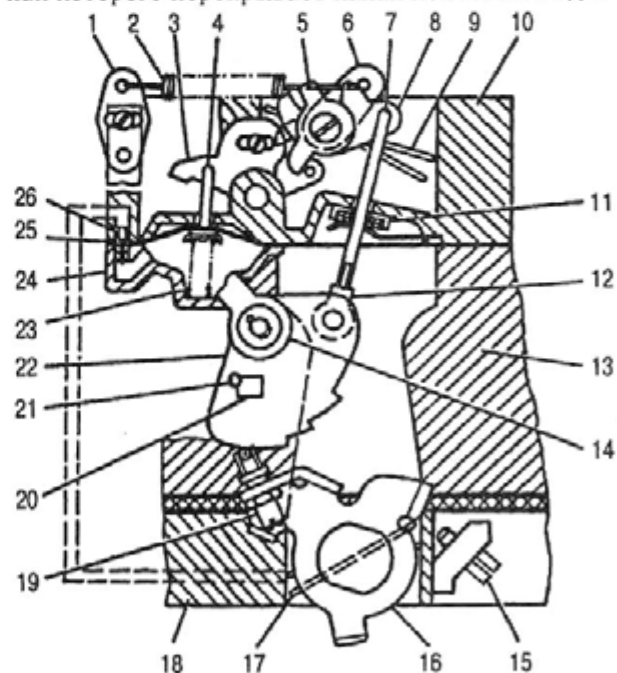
Система пуска и прогрева холодного двигателя: 1, 5, 6 и 16 - рычаги; 2 - пусковая пружина; 3 - промежуточный рычаг; 4 - тяга пневмокорректора; 7 - тяга; 8 - секторный рычаг; 9 - воздушная заслонка; 10 - крышка карбюратора; 11 - уплотнительный элемент; 12 - регулировочная муфта; 13 - корпус поплавковой камеры; 14 - рычаг привода воздушной заслонки; 15 - упорный винт дроссельной заслонки первичной секции карбюратора; 17 - дроссельная заслонка первичной секции карбюратора; 18 - корпус смесительных камер; 19 - винт с роликом; 20 - упор; 21 - штифт; 22 - профильный рычаг; 23 - пружина пневмокорректора; 24 - крышка пневмокорректора; 25 - диафрагма; 26 - жиклер пневмокорректора
